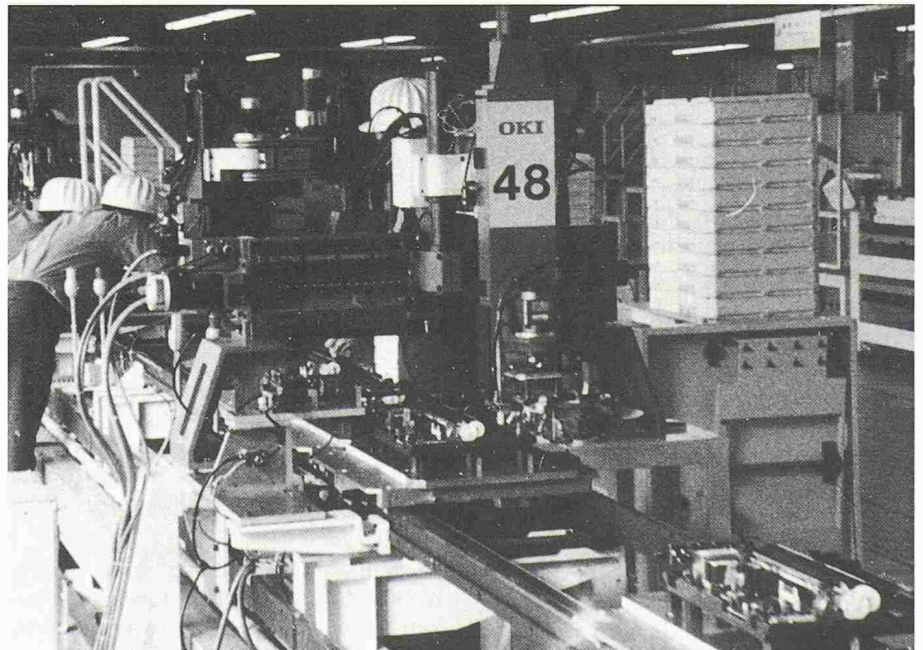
Automatisches Montagesystem für Drucker (Werkbild OKI-DATA)
